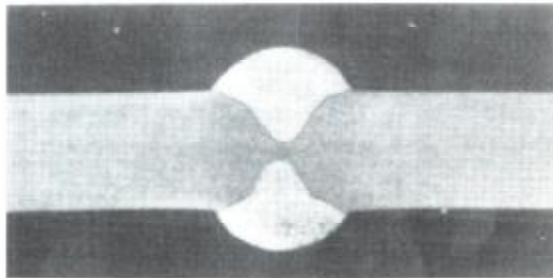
Bindefehler durch ungenügende Durchschweißung.
